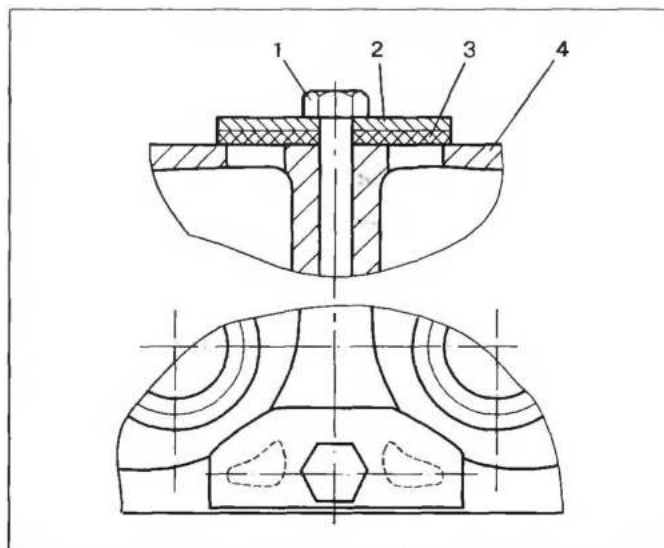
Способ глушения окон рубашки охлаждения в головке блока цилиндров:
